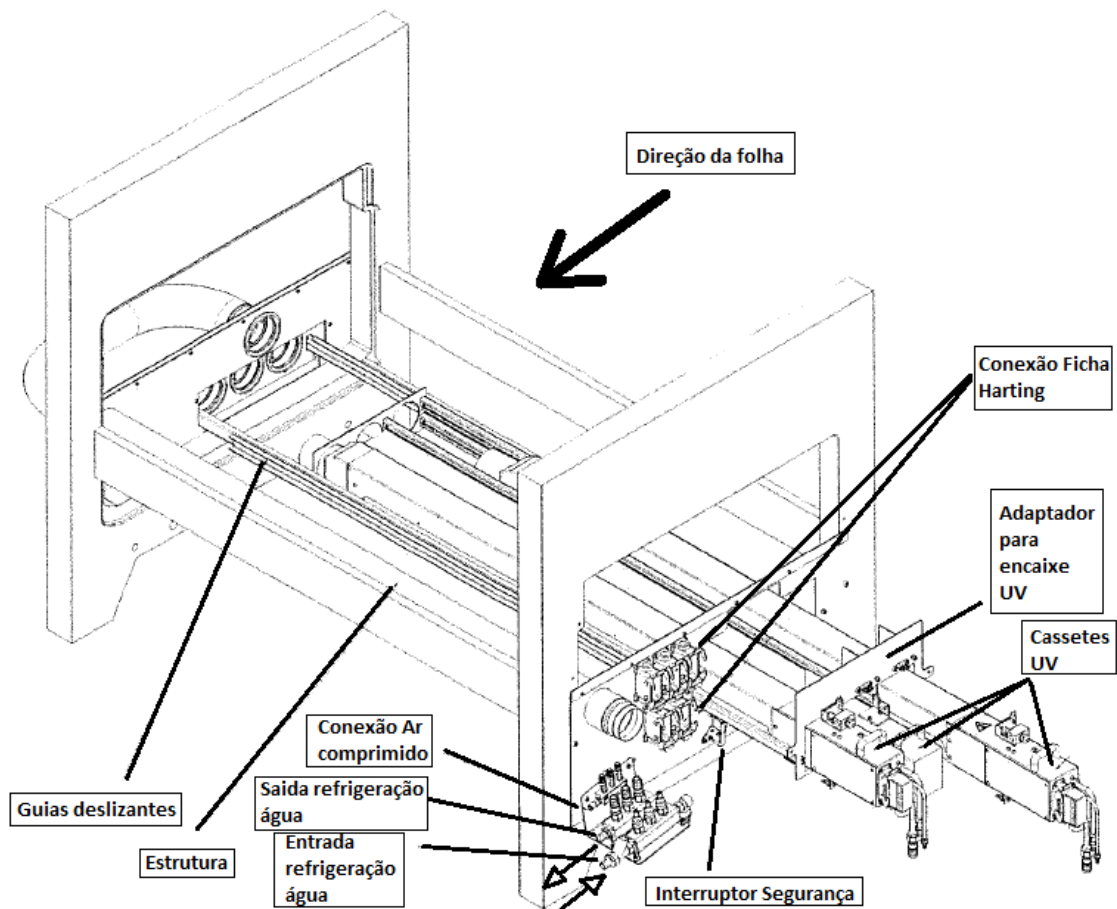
26- Desenho técnico da zona da cassete de secagem
